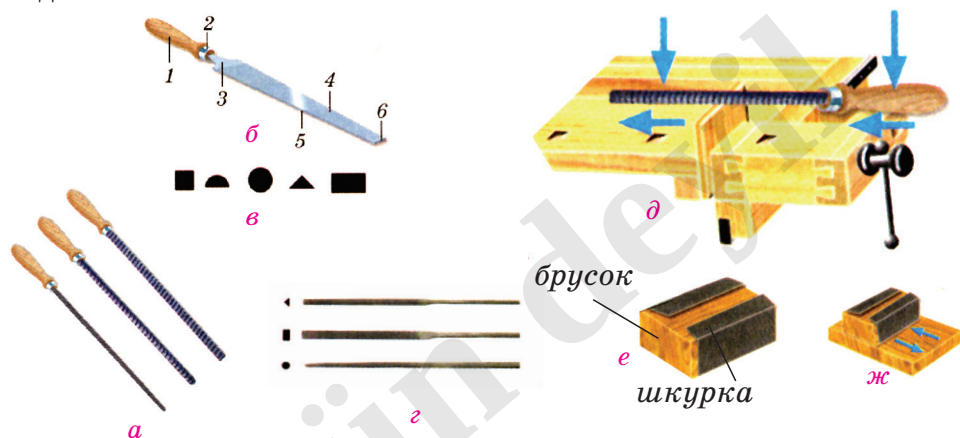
Инструменты и приспособления* для зачистки деталей из древесины:
